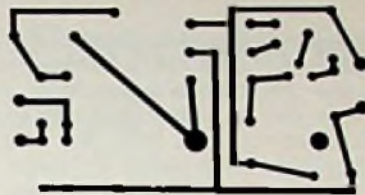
Printzeichnung der Netzteilplatine (Maßstab 1 : 2)
